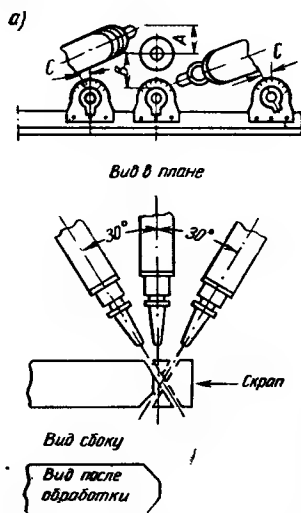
Схема обработки кромки Х-образного шва трех-резакowej горелкой
